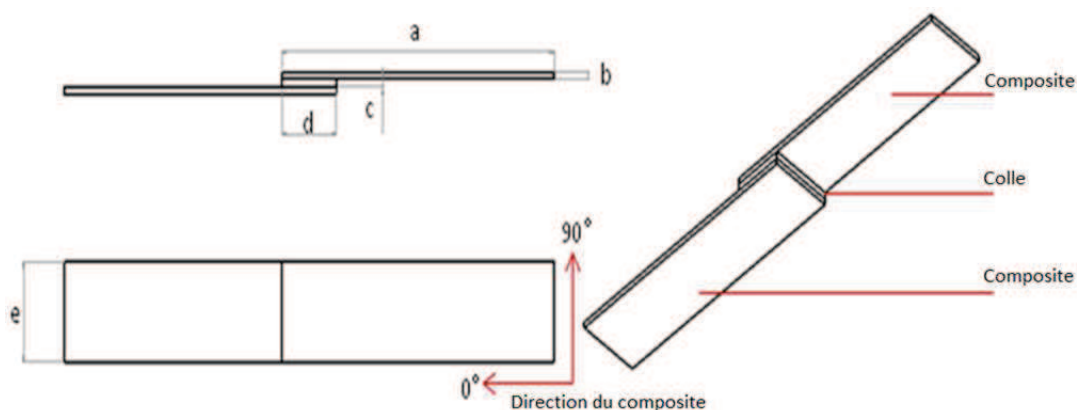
Géométrie des éprouvettes pour les essais de simple recouvrement
